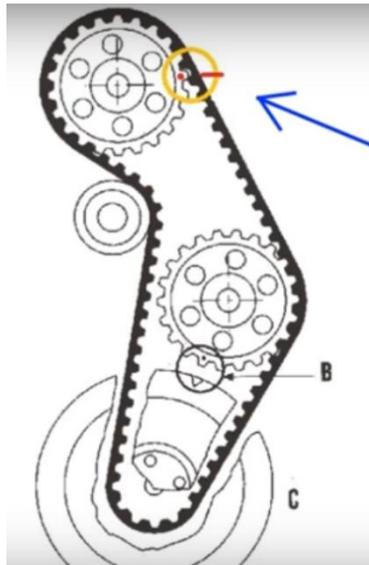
Engranaje árbol de levas / Fuente: www.todomotores.cl
